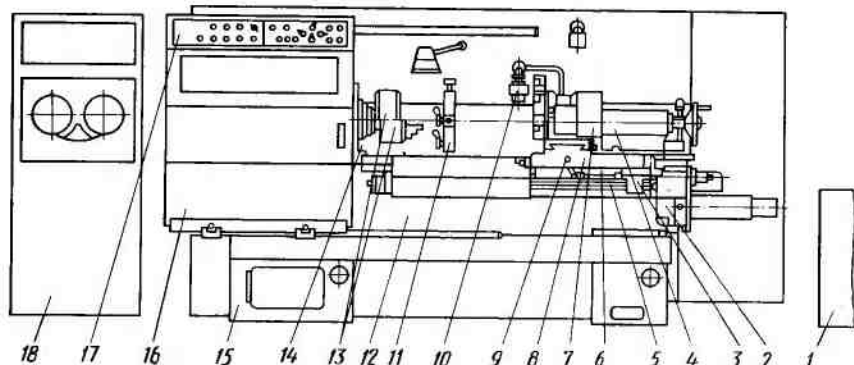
Общий вид токарного станка мод. 16K20Ф3 с ЧПУ
